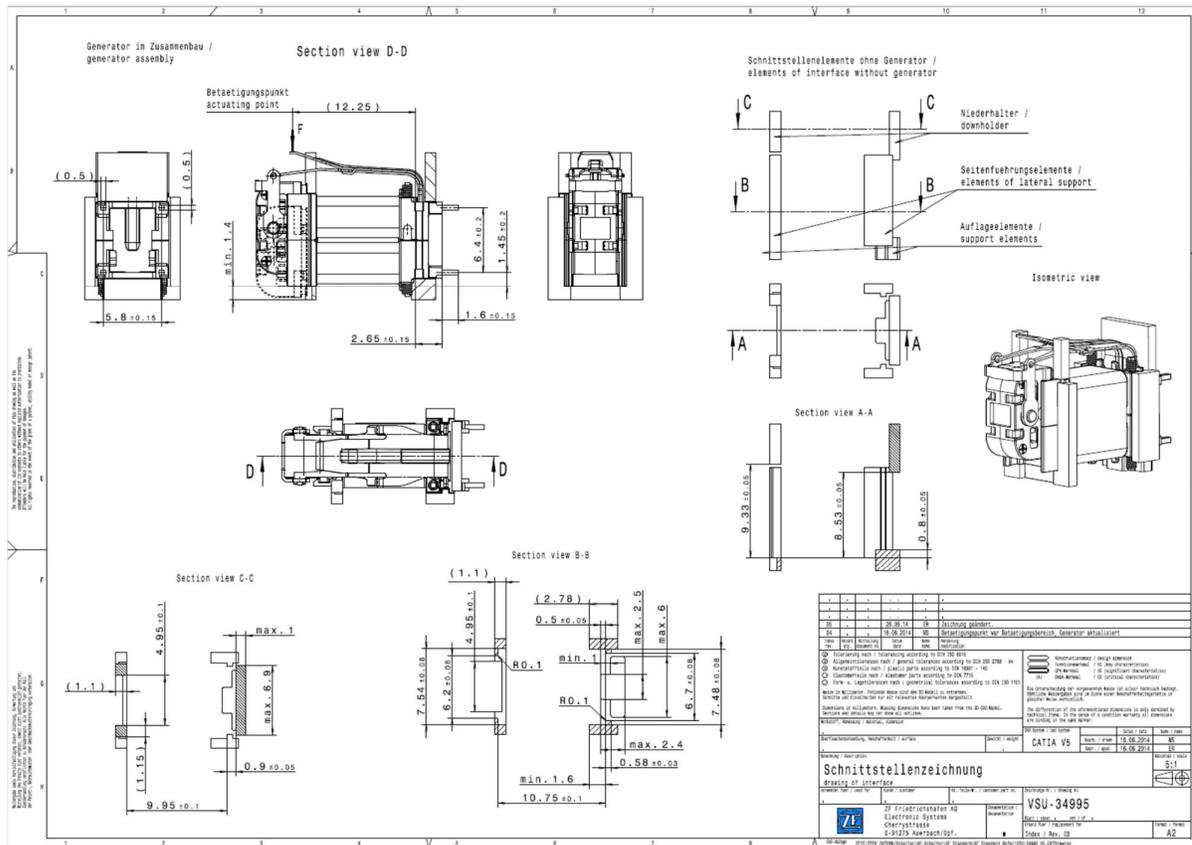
Einbau- und Montagehinweise / Mounting- and assembly instructions
